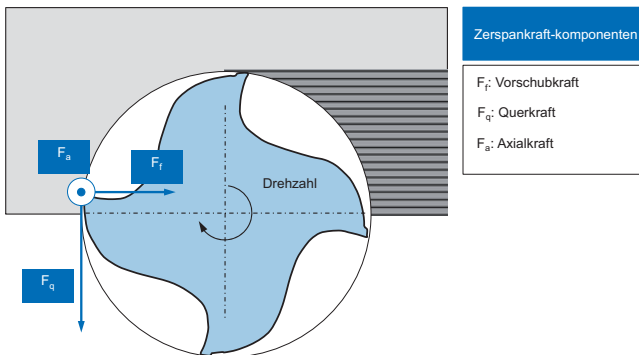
Zerspankraftkomponenten beim Fräsen
